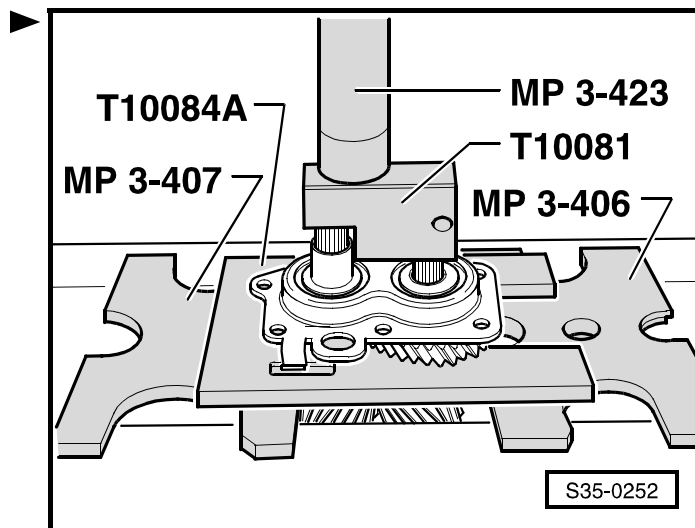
Извлечение втулки роликоподшипника с шестерней для 4-ой передачи ►
